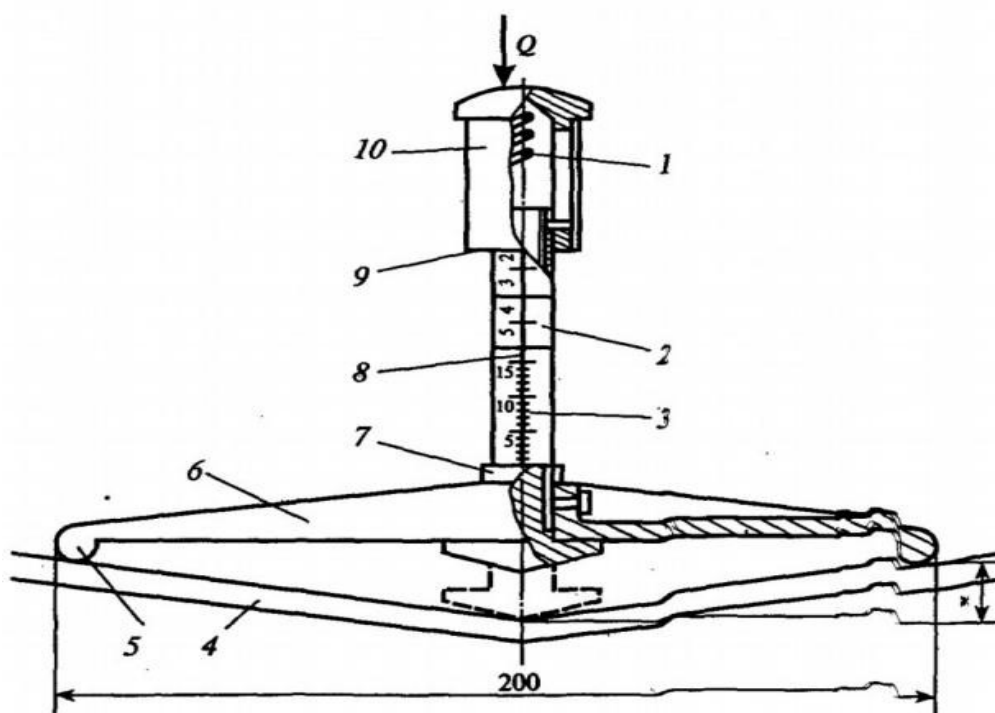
Приспособление для контроля натяжения ремня ременной передачи:
